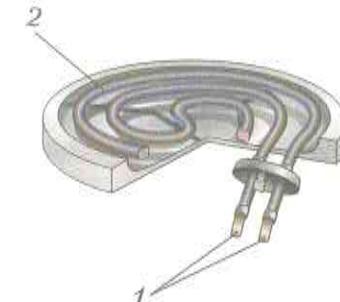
Трубчатый электронагревательный элемент (ТЭН):
